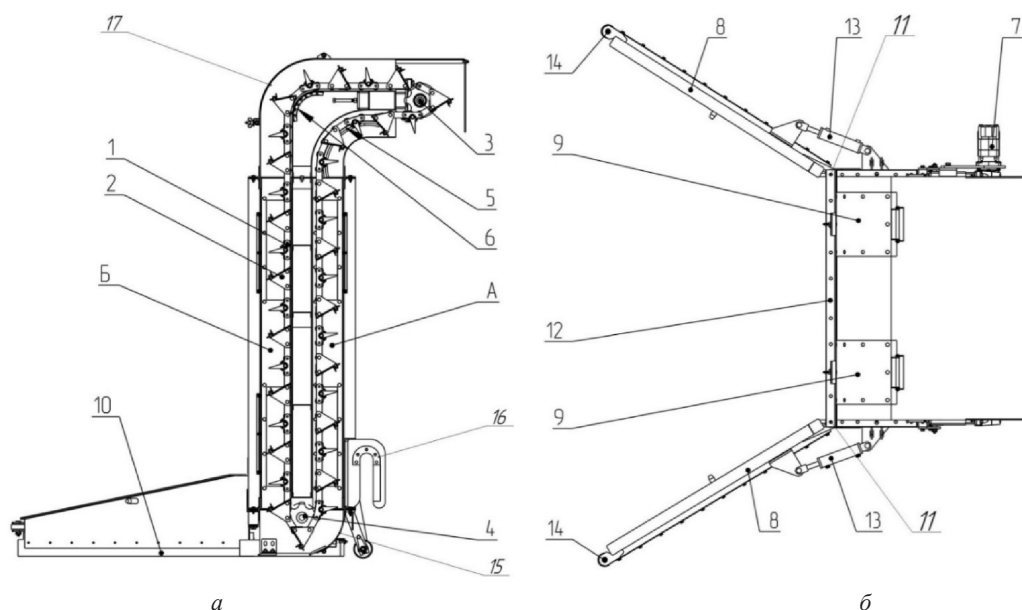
Скрепер-элеватор в разрезе (а) и вид сверху (б): А – подающий канал; Б – возвратный канал; 1 – цепь роликсовая; 2 – планки; 3 – ведущий вал; 4 – ведомый вал; 5 – направляющие подающей ветви; 6 – направляющие возвратной ветви; 7 – гидромотор; 8 – отвал; 9 – крышки откидные; 10 – пластины подчищающие; 11 – оси; 12 – кожух; 13 – гидроцилиндр; 14 – упоры роликсовые; 15 – подборщик; 16 – кронштейн специальный; 17 – бокс выгрузной
